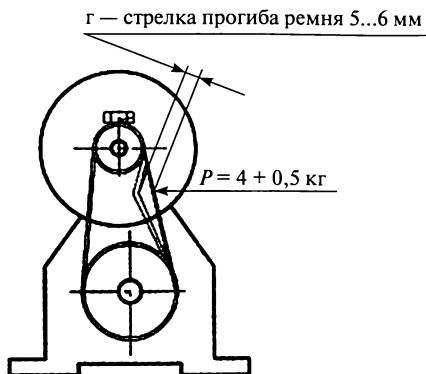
Схема регулирования натяжения ремня привода вентилятора
